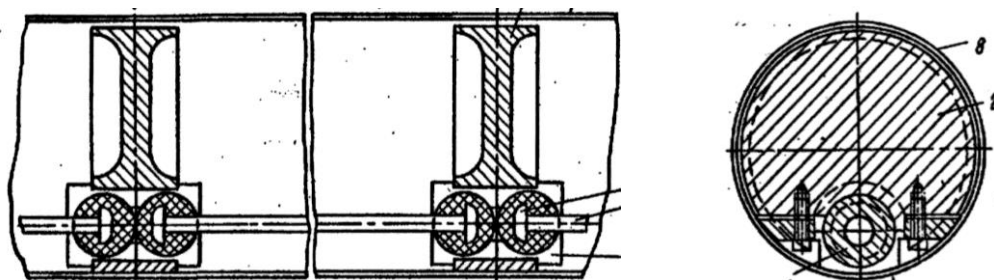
Шарнірний трубчатий скребковий конвеєр
